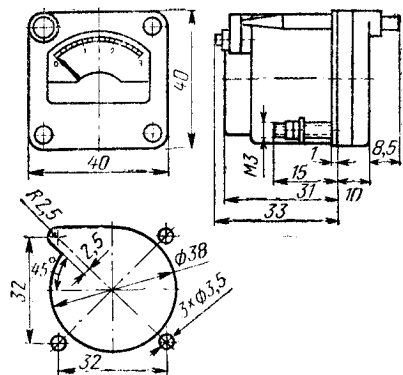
Габаритный чертеж прибора типа М4230.
